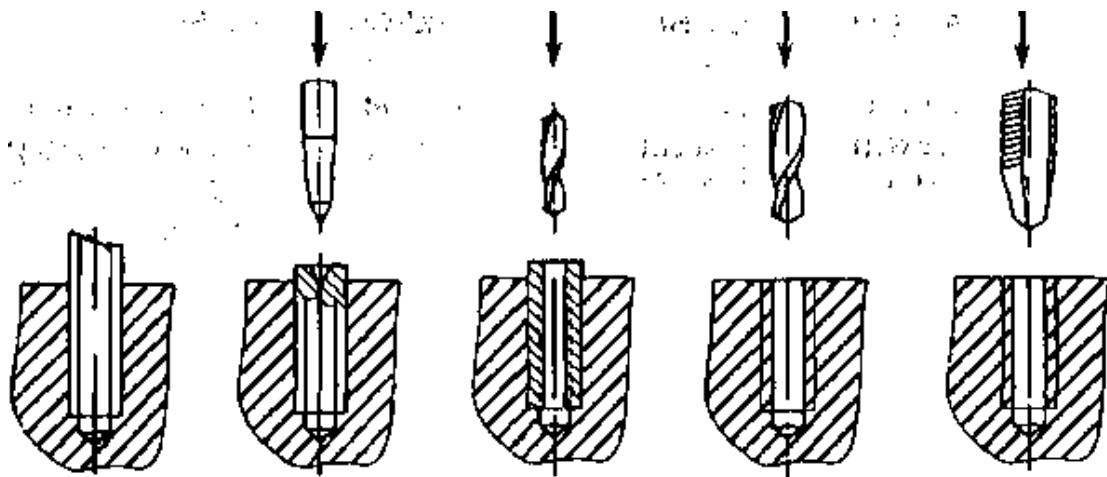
Схеми висвердлювання обломаної шпильки (болта):
